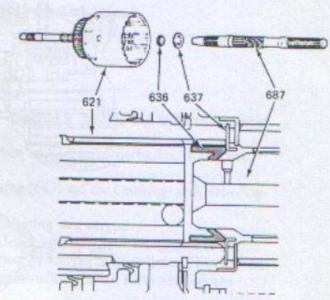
Inputgehäuse-an-Outputwellen-Lippendichtung
